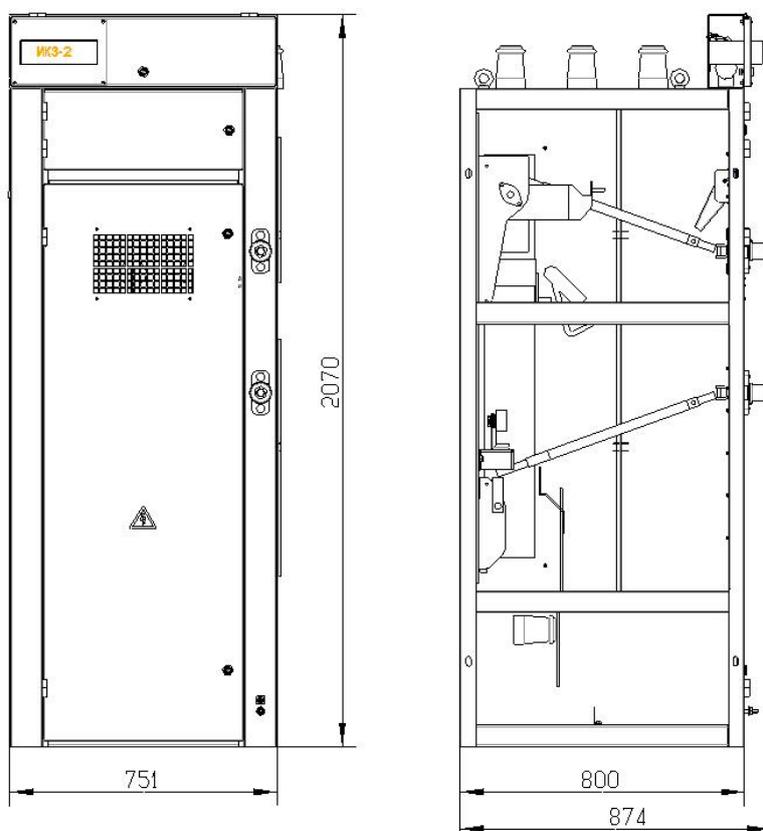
Общий вид и габаритные размеры камеры КСО-305ЭФ
